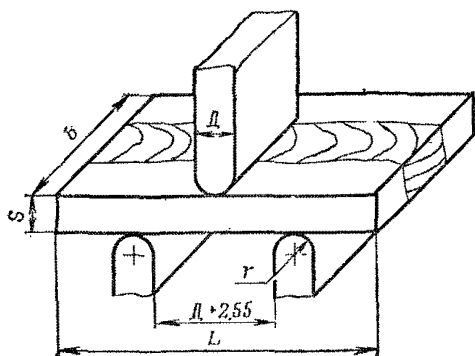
Схема испытания сварного шва на загиб. Образец типа, представленного на рис. 3.
